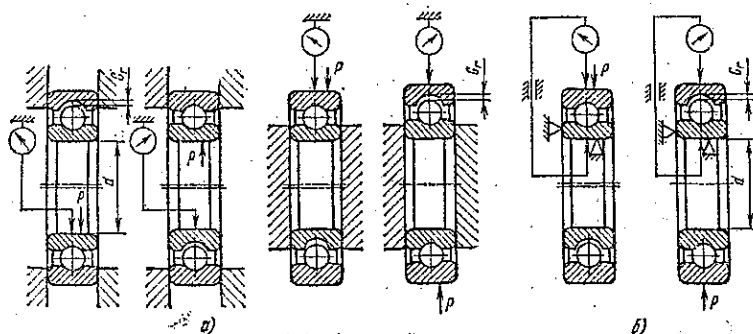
Схема измерения радиального зазора: а — с креплением колец по торцу; б — без крепления колец; G_r — радиальный зазор; P — измерительная нагрузка
